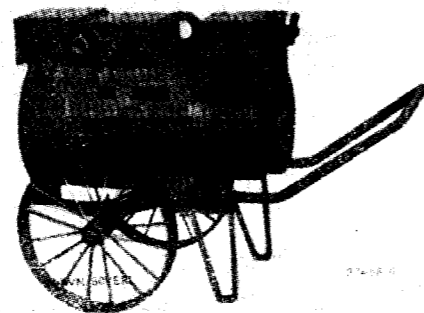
La dinamo de soldadura Brown Boveri montada en un carrito.
